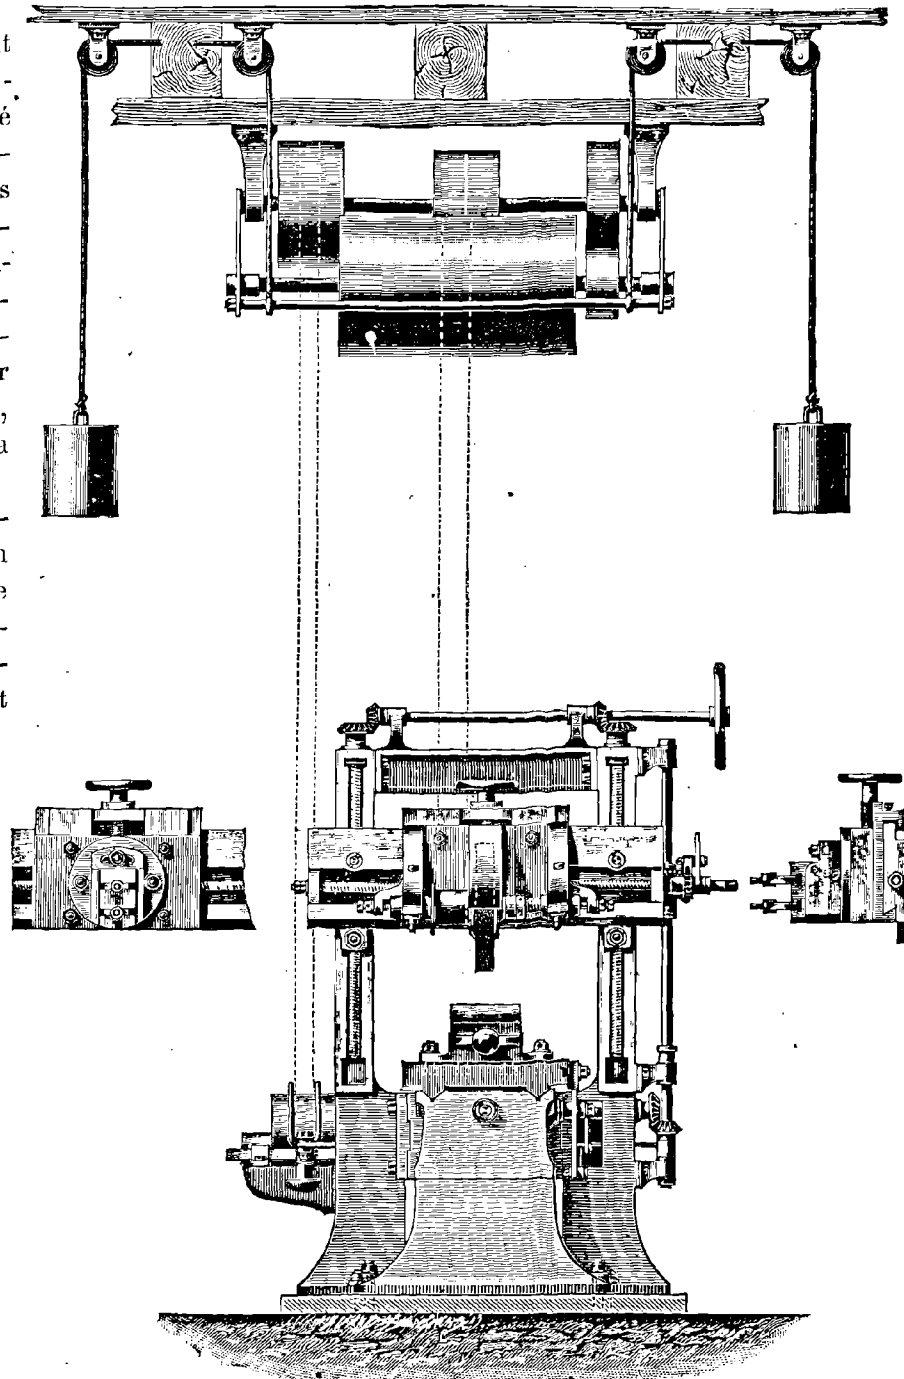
Machine à rectifier les surfaces planes de M. Lucas.
